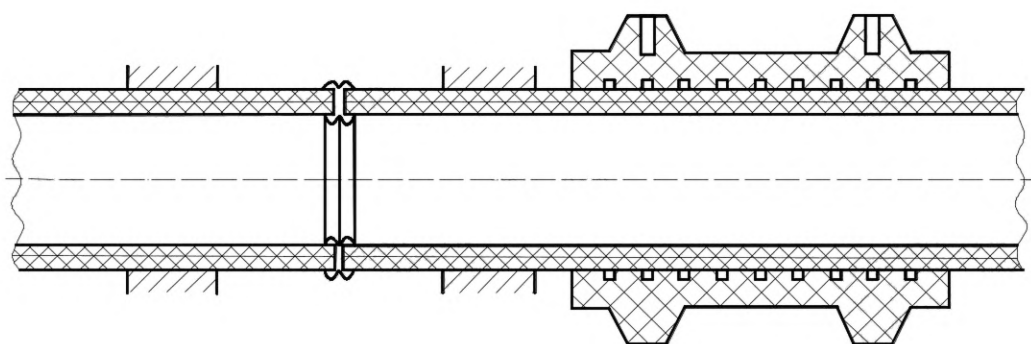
Осадка стыка до образования сварного соединения
